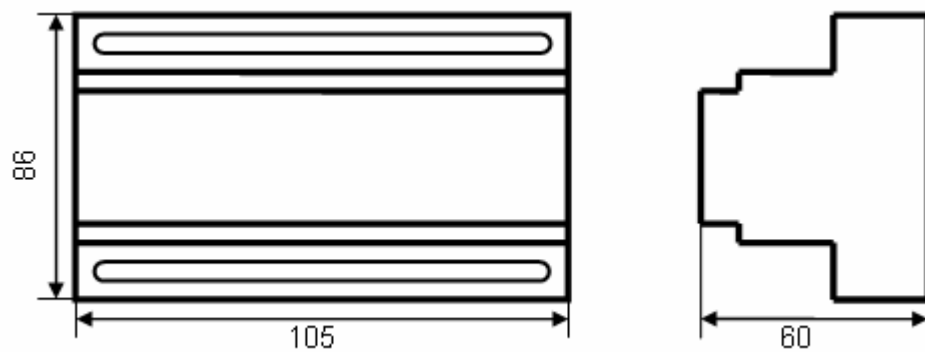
Габаритный чертеж контроллера в негерметичном исполнении
